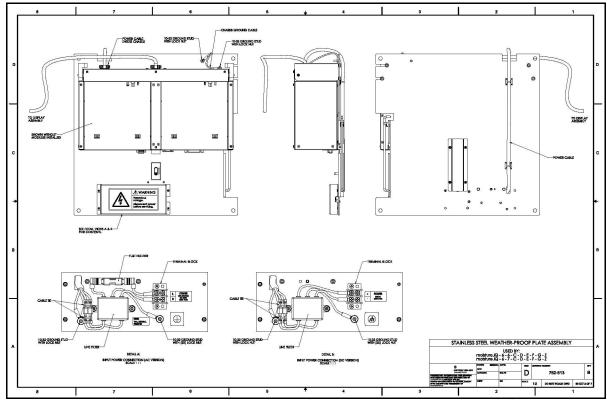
Conjunto de placas WP (desenho 752-513\_revB, SH 2 de 5)
